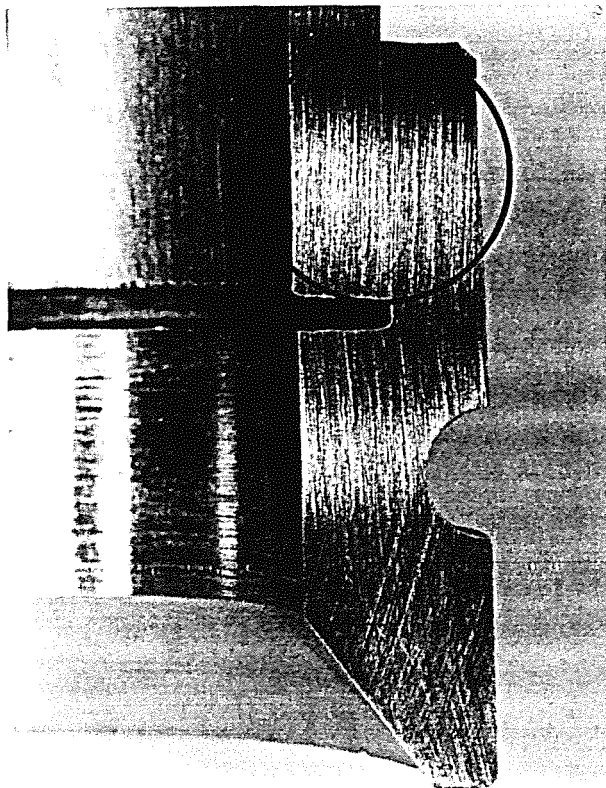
Sección de la soldadura del conector suministrado por la Empresa B. La unión se ha realizado por soldadura fuerte.
